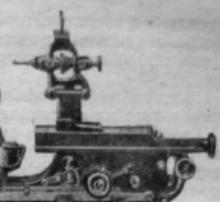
Настольный круглошлифовальный станок Дикси для наружной шлифовки.
